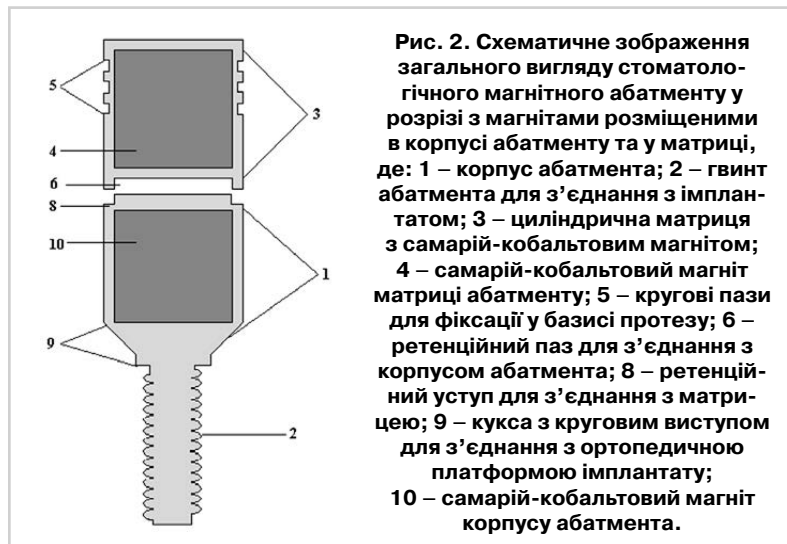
Схематичне зображення загального вигляду стоматологічного магнітного абатменту у розрізі з магнітами розміщеними в корпусі абатменту та у матриці, де: 1 – корпус абатменту; 2 – гвинт абатменту для з'єднання з імплантатом; 3 – циліндрична матриця з самарій-кобальтовим магнітом; 4 – самарій-кобальтовий магніт матриці абатменту; 5 – кругові пази для фіксації у базисі протезу; 6 – ретенційний паз для з'єднання з корпусом абатменту; 8 – ретенційний уступ для з'єднання з матрицею; 9 – кукса з круговим виступом для з'єднання з ортопедичною платформою імплантату; 10 – самарій-кобальтовий магніт корпусу абатменту.
